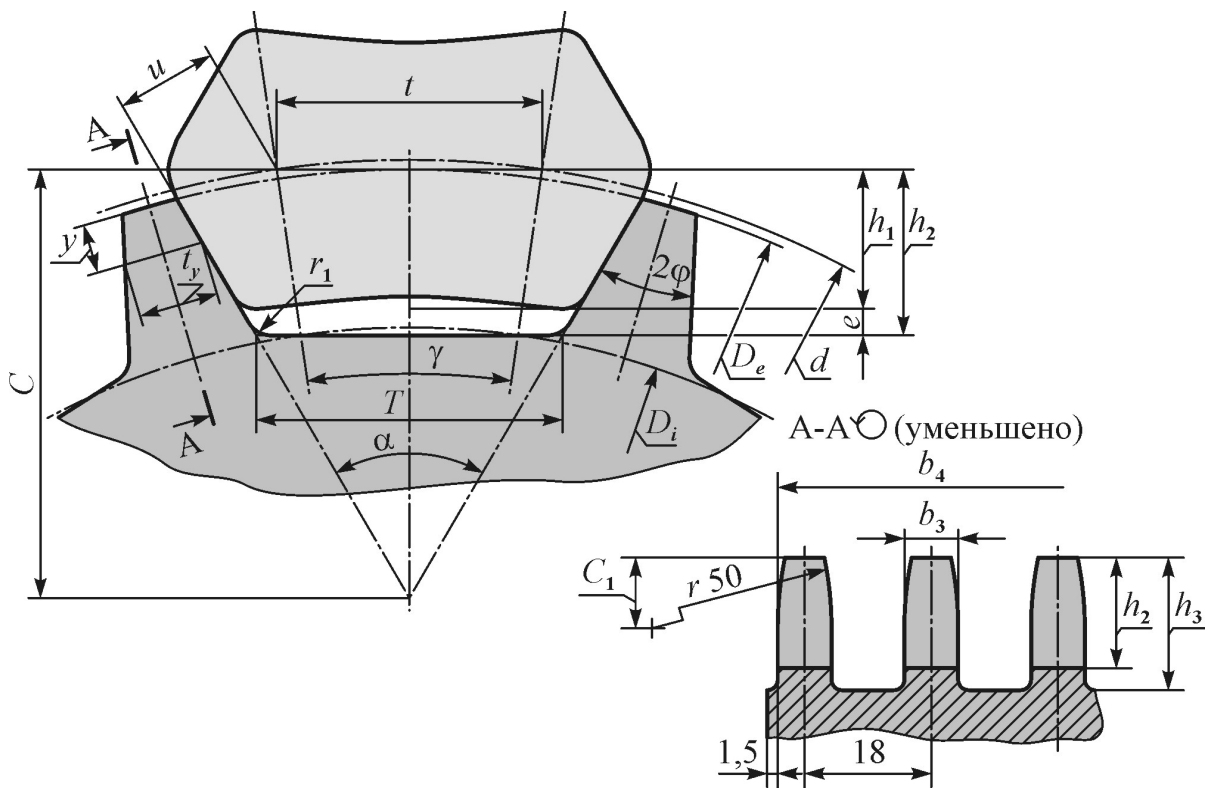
Профиль зубьев звездочки для зубчатой цепи типа ПЗ-2
